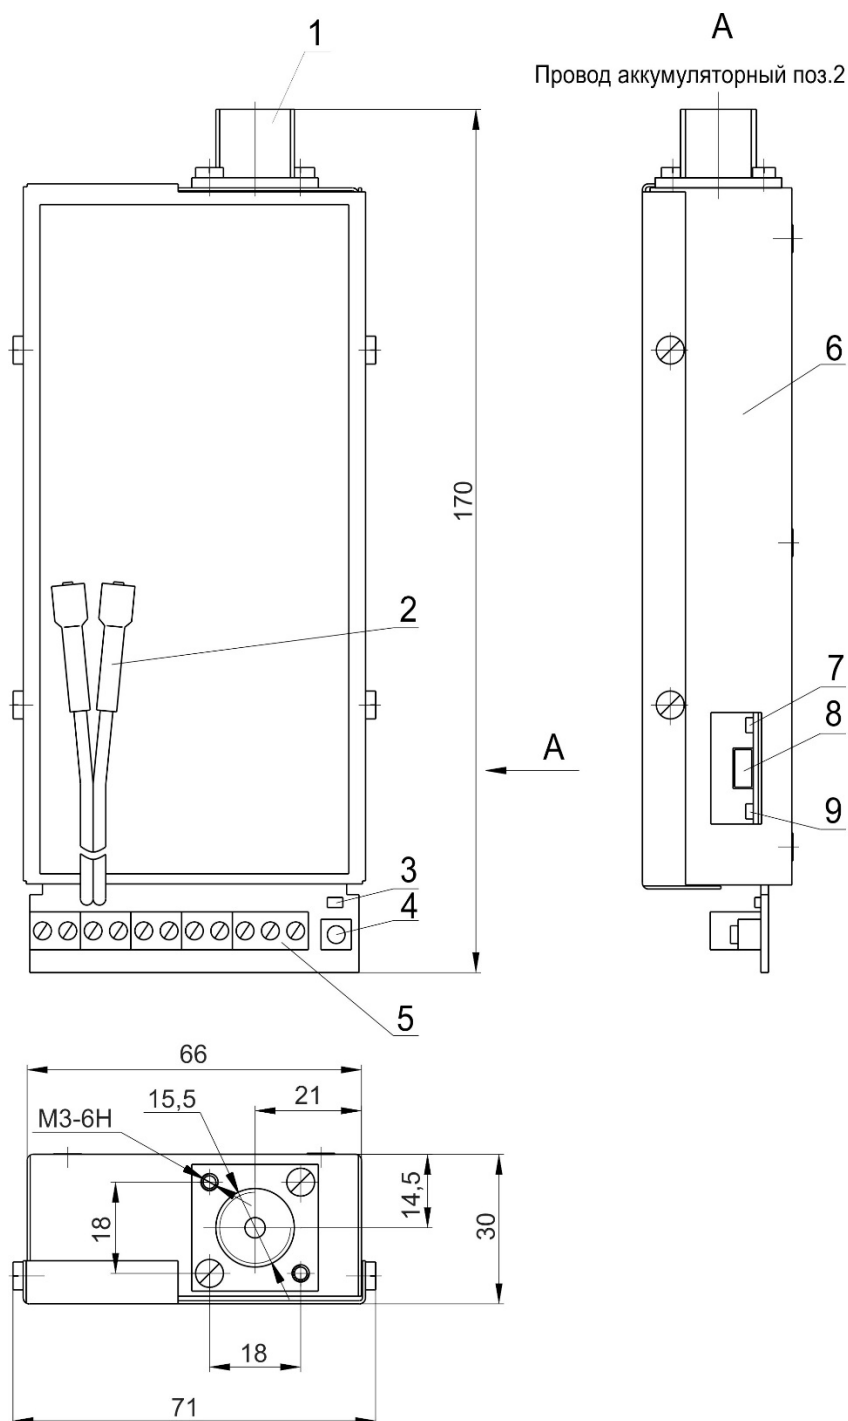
Габаритные размеры передатчика и расположение элементов
